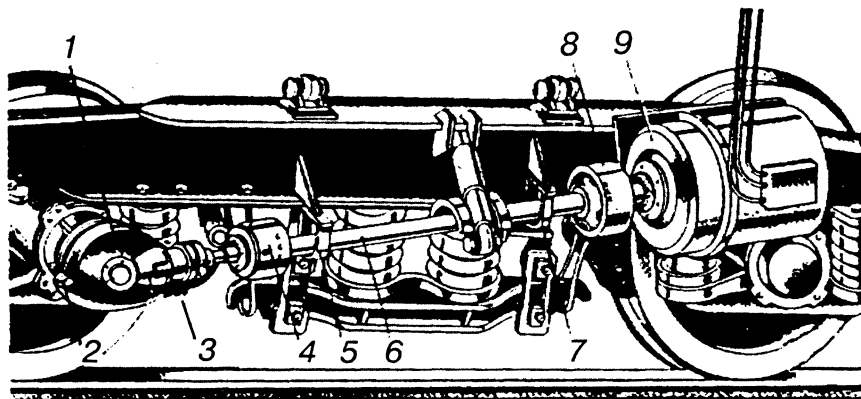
Расположение редукторно-карданного привода от торца оси на тележке:
